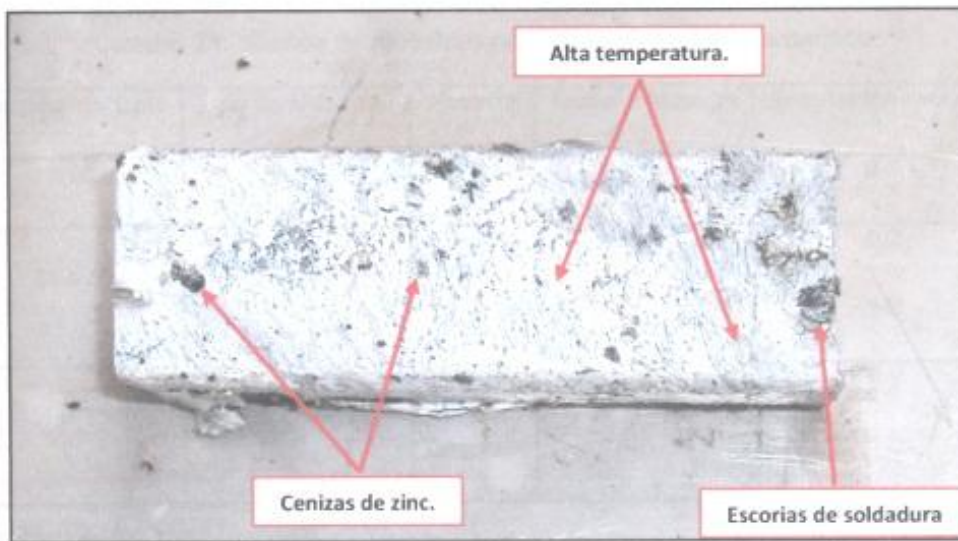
Fallas de recubrimiento en el tubo cuadrado de 1".
